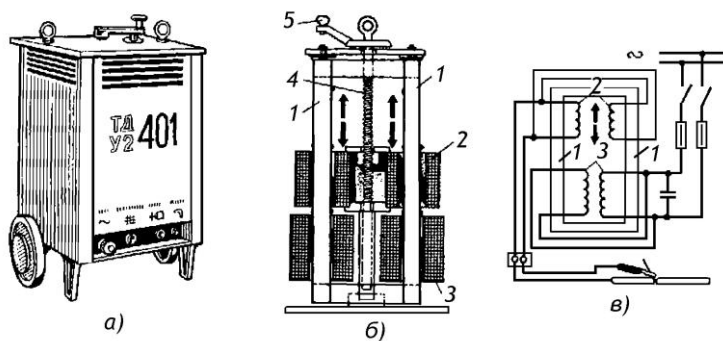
Сварочный трансформатор ТД-401У2, где а – общий вид, б – вид без кожуха, в – электрическая схема.
